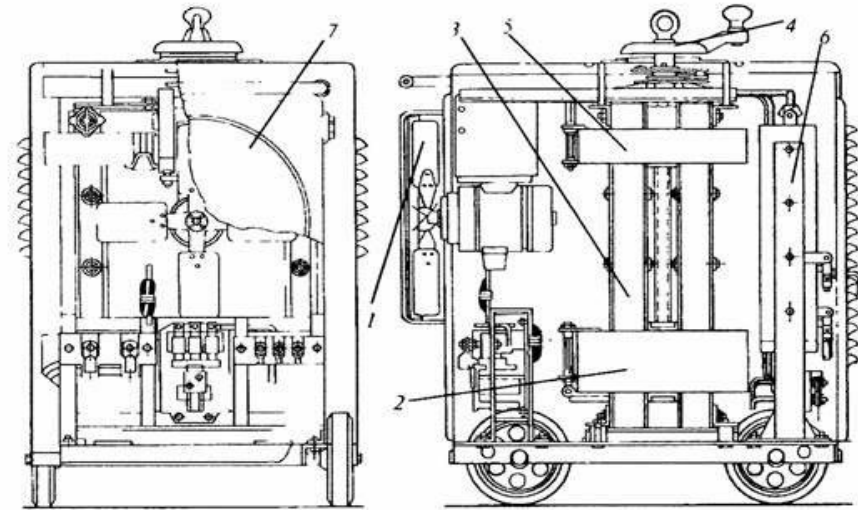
Конструктивная схема сварочного выпрямителя ВСС-300.
